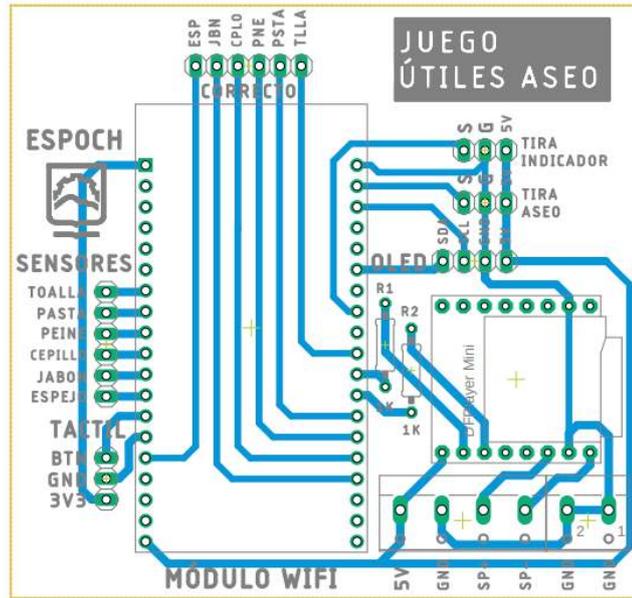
Diseño de la placa PCB del módulo de aseo
